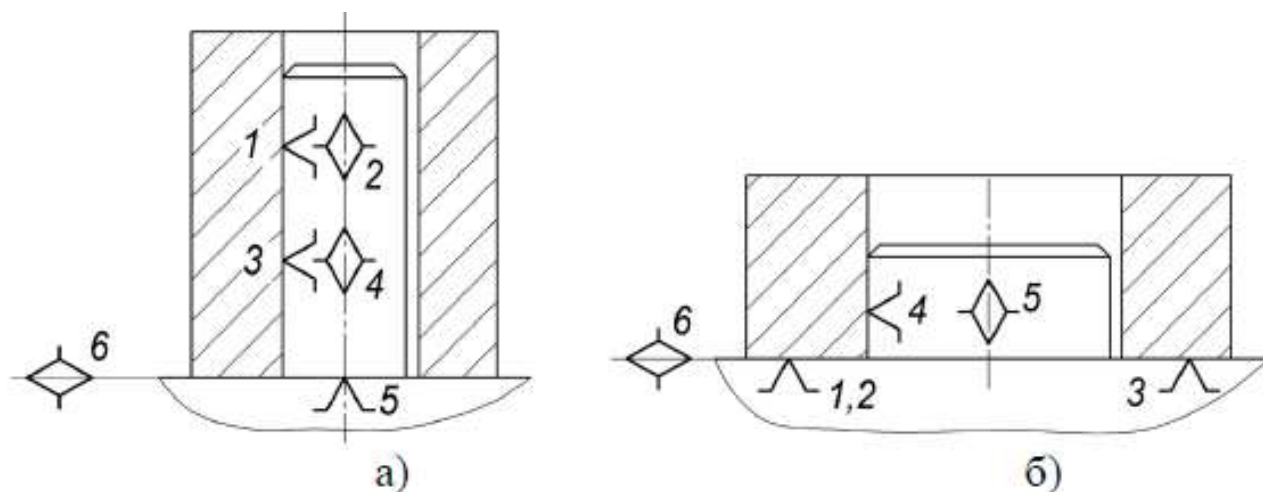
Схеми базування за допомогою двох площин та зовнішньої циліндричної поверхні
